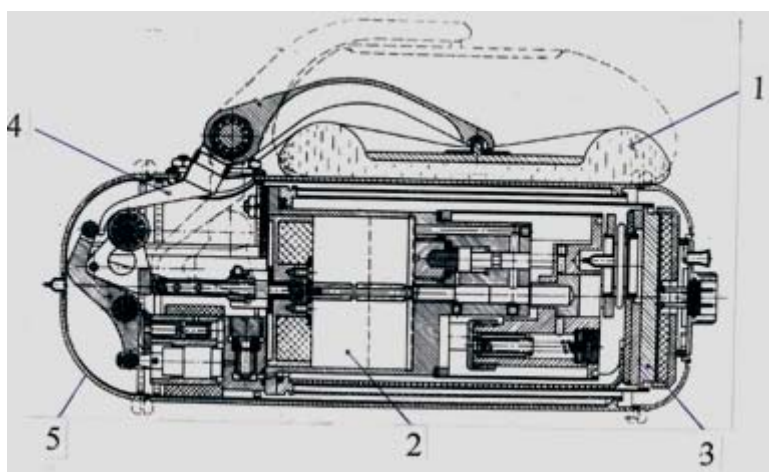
Устройство КИЖ СЧИ ОЛЖ «Микрон-М»: 1 – НУК; 2 – паровая машина; 3 – нагреватель; 4 – рычажный механизм; 5 – корпус
